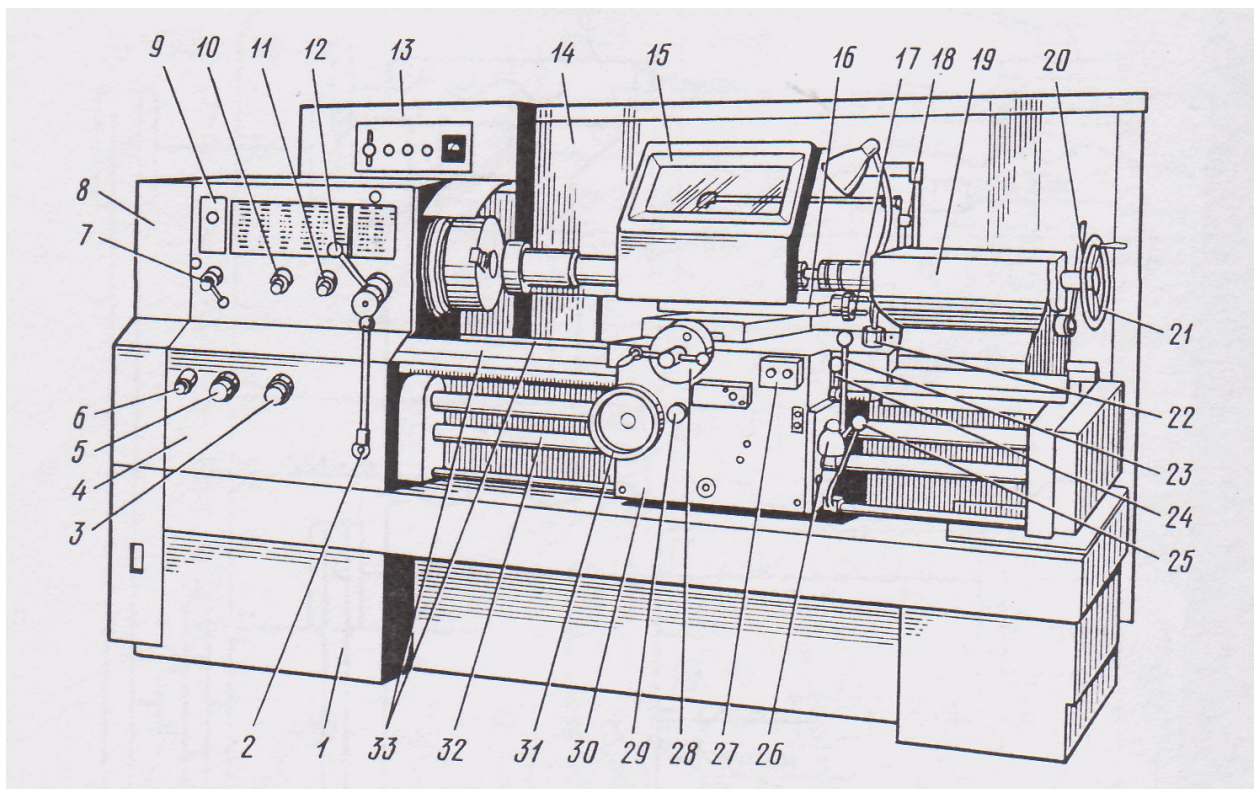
Общий вид и размещение органов управления токарно-винторезного станка модели 16К20:
